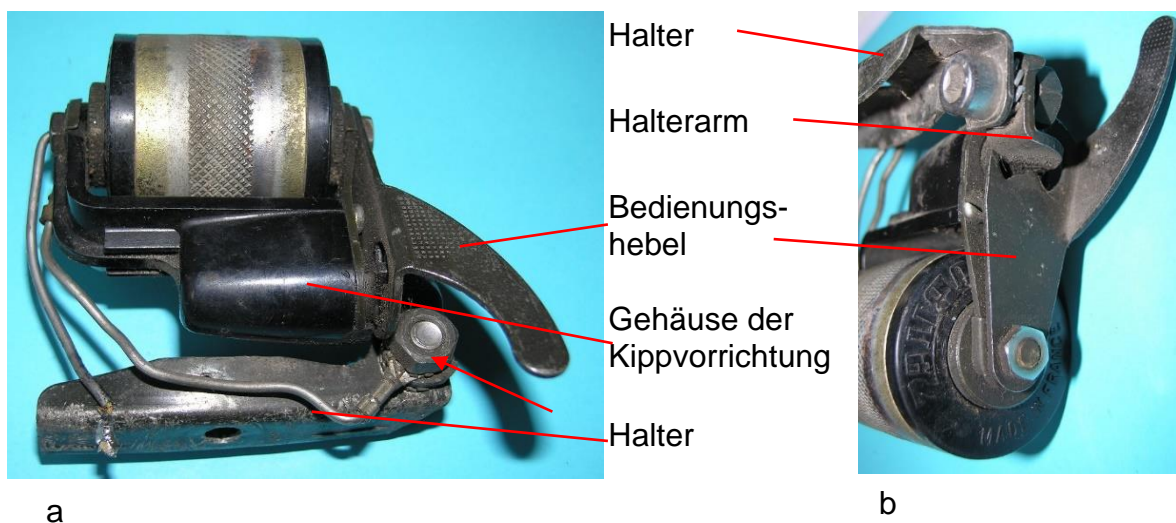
Anbringung des Halters: a) Halterbefestigung, b) Seitenansicht
